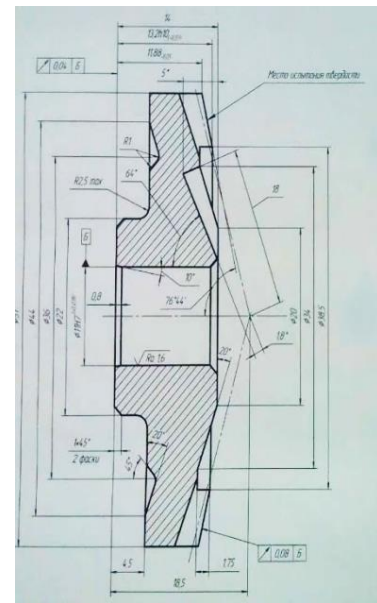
Чертеж колеса зубчатого ИДФР.722333.001
